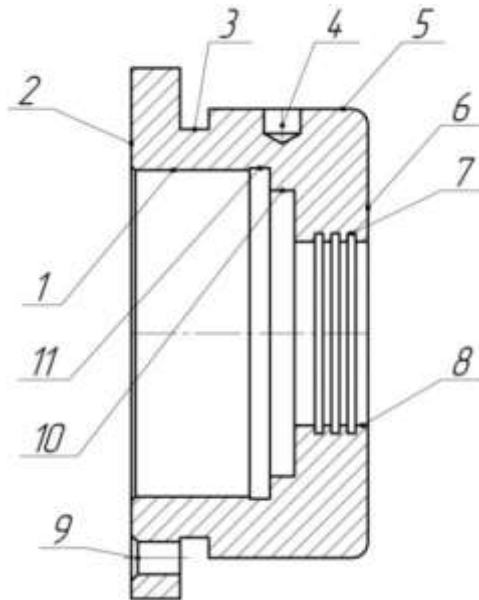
Оброблювані поверхні деталі стакан підшипника п'яти
